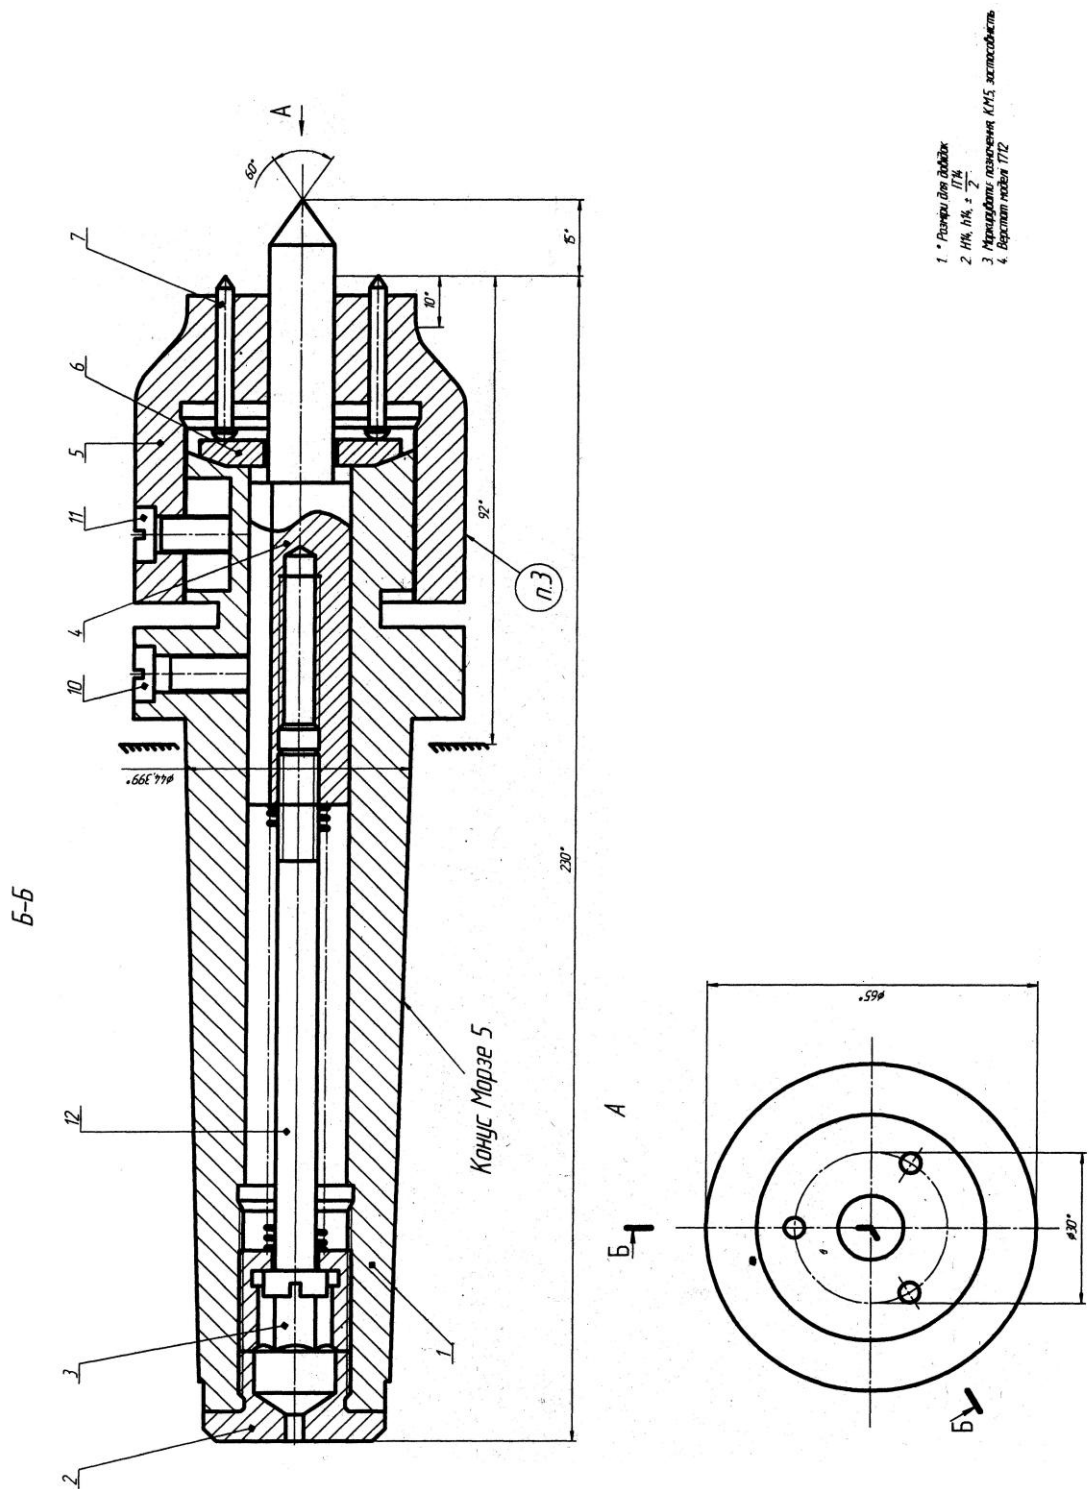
Штирковий плаваючий центр призначений для центрування та обертання оброблюючої деталі при обробці на токарних та шліфувальних верстатах
